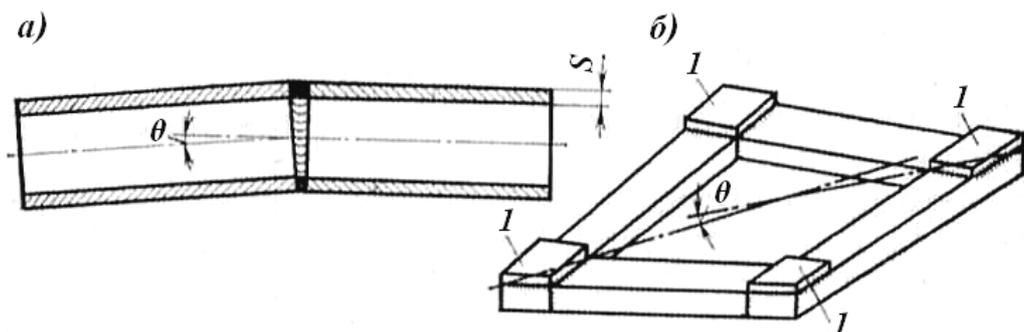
Перемещения в сварных деталях, вызывающие увеличение припуска на механическую обработку
